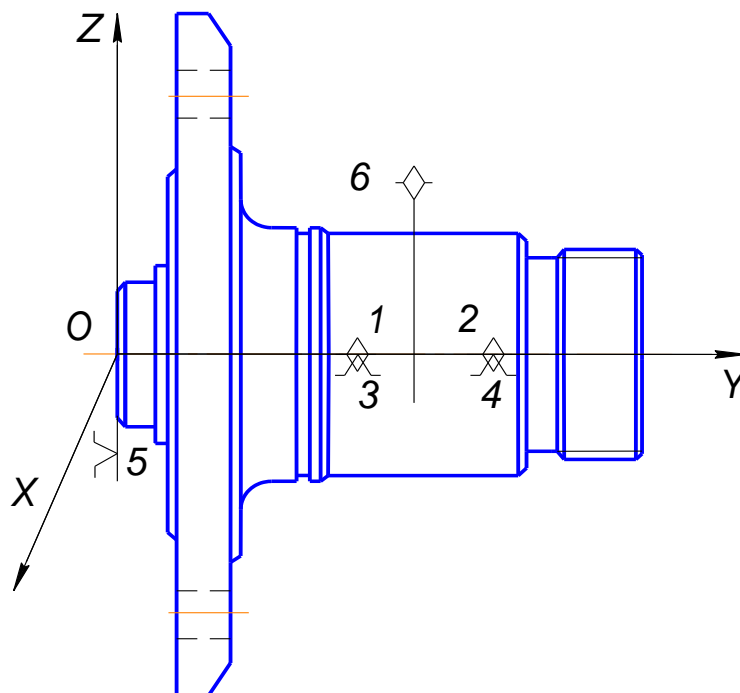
Схема базирования заготовки в приспособлении
